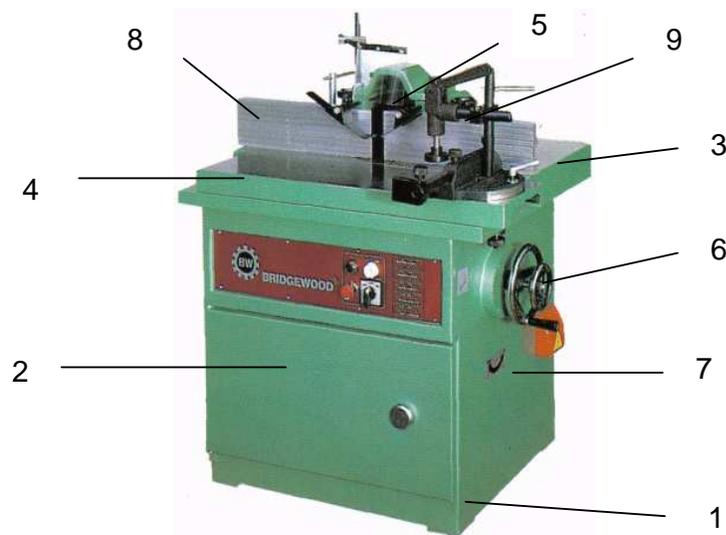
Partes de la Máquina Tupí. Tomado de [13]
